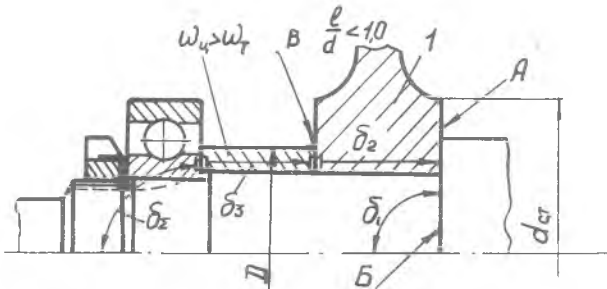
Установка на валу колеса с короткой ступицей, кольца и подшипника
